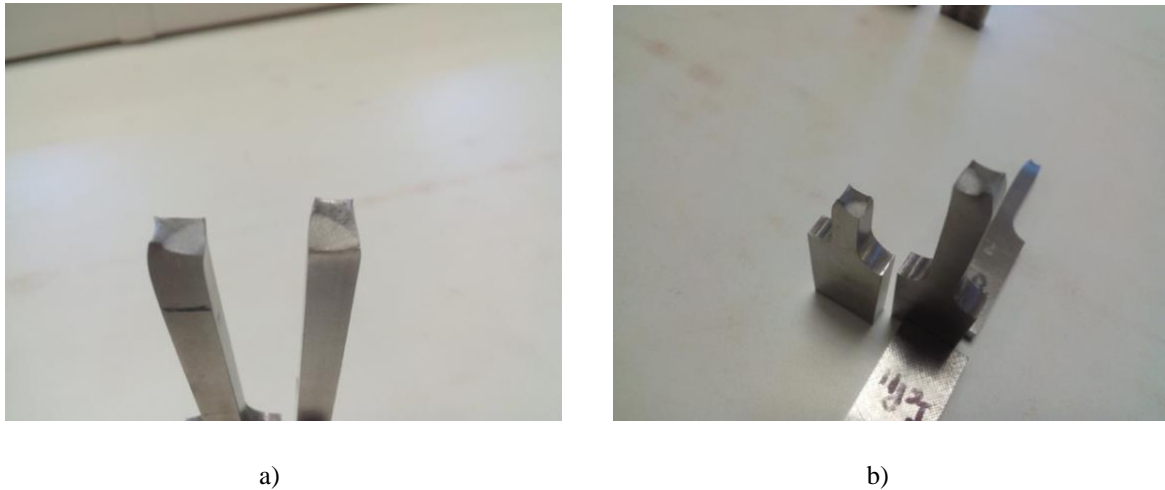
Superfície de fratura dúctil do aço R304 sujeito a) à fadiga e b) à fadiga sob corrosão
